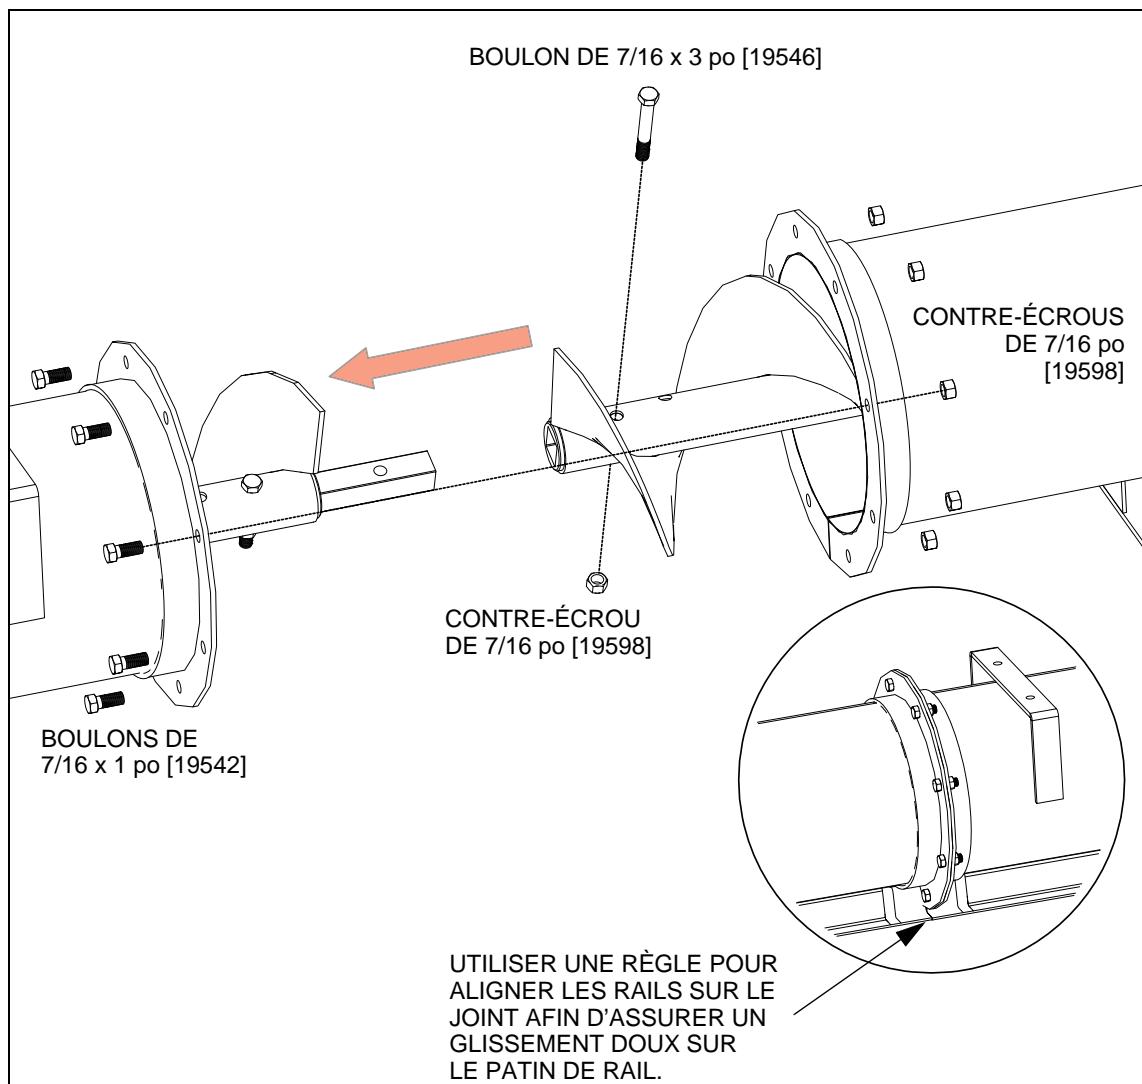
Raccordement des sections de tube de la tarière et des déflecteurs
